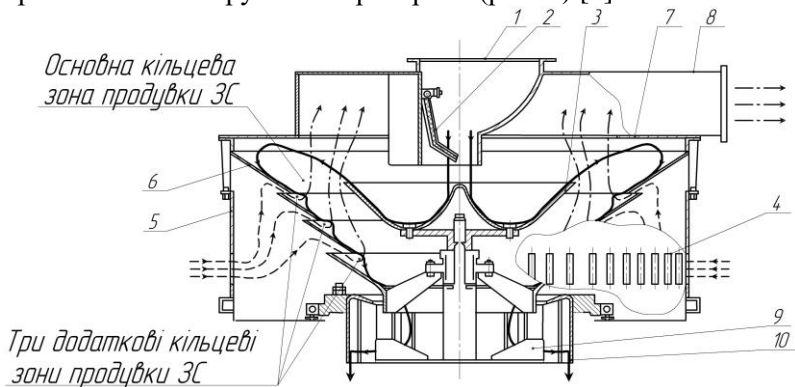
Конструктивна схема розробленого віяло-кільцевого конусно-каскадного ПСП: 1 - патрубок завантажувальний; 2 - клапан дозуючий; 3 - розкидач тарілчастий; 4 - вікна повітрозабірні; 5 - кожух сепаратора; 6 - конус каскадний складений; 7 - діафрагма; 8 - патрубок відвідний; 9 - розкидач дисковий; 10 - блок решітний; \longrightarrow – рух зернового матеріалу; $-\ - \blacktriangleright$ – повітряного потоку; $- \cdot \blacktriangleright$ – повітряного потоку з відокремленими легкими домішками
